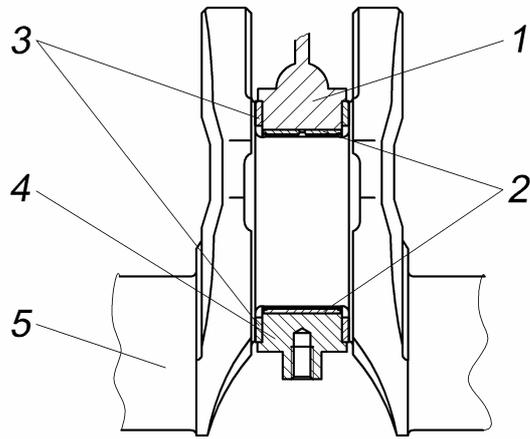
Средний (упорный) подшипник коленчатого вала:
